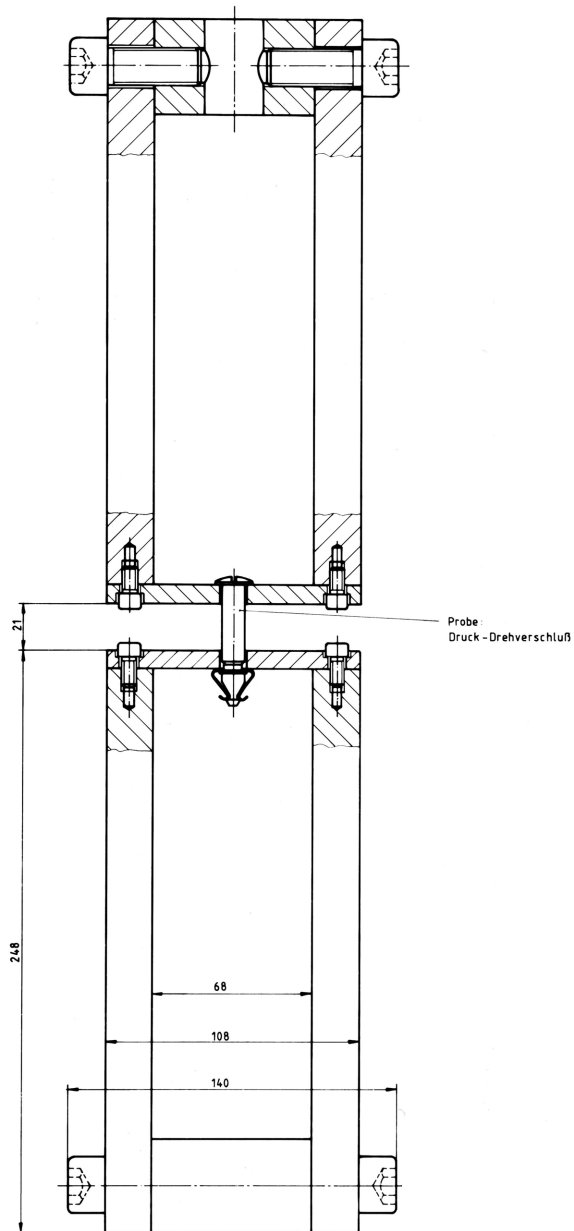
Probenaufnahme für Druck-Drehverschlüsse
